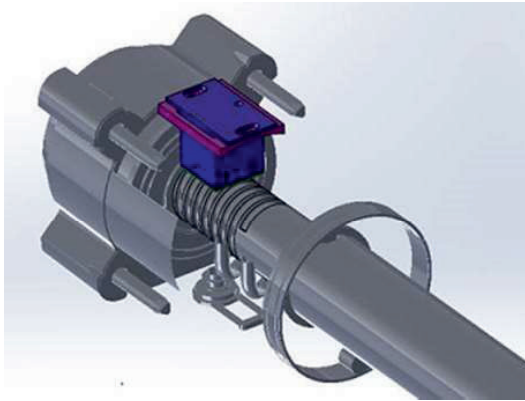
3D-Ansicht des Sensorträgers für die rotative Messung.
